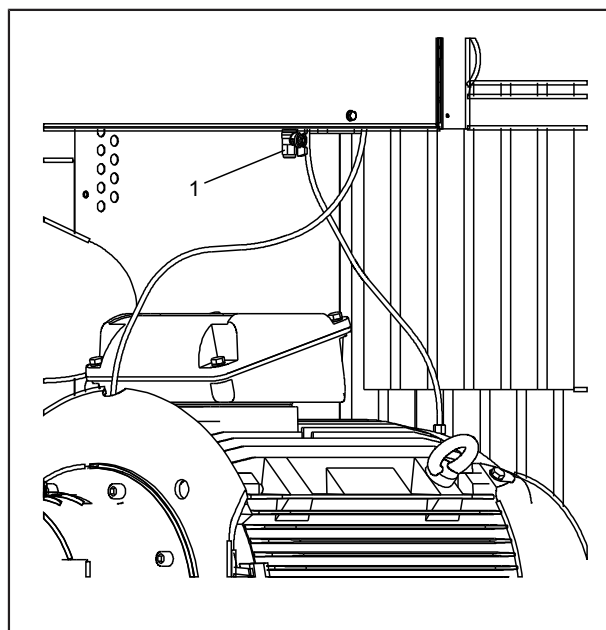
Position af udluftningsventil i luftkølet kompressor anlæg
